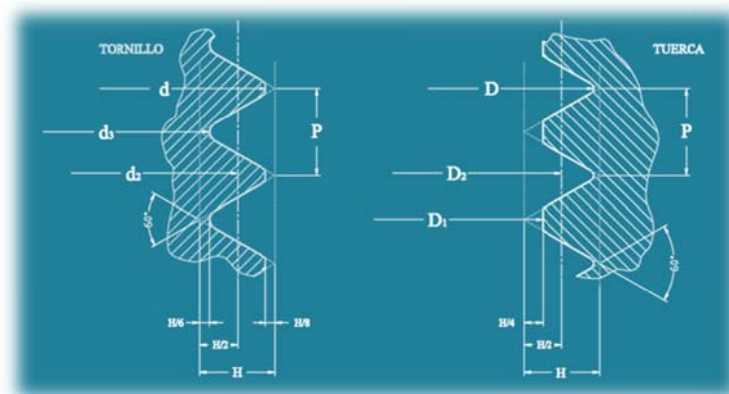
En la figura se muestran los parámetros geométricos que definen la rosca de un tornillo (derecha) y la de una tuerca o rosca hembra (izquierda)
